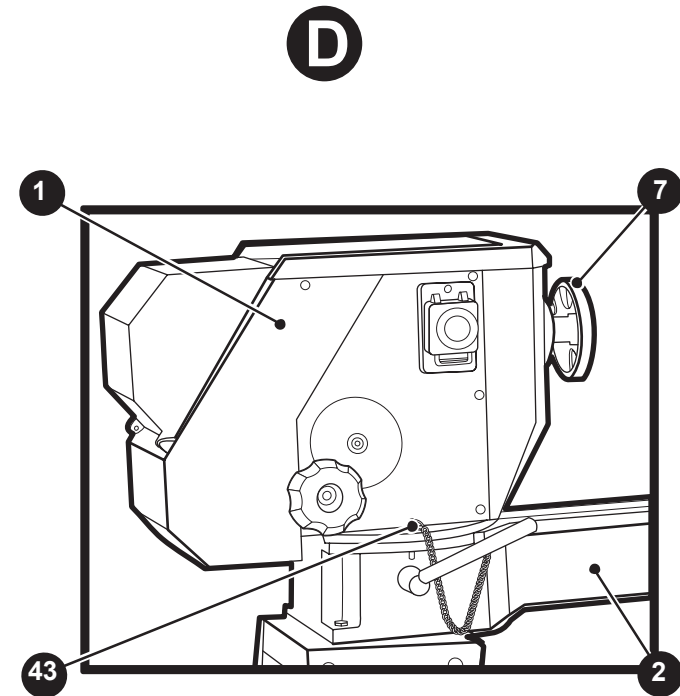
Рисунок D — общий вид станка с установленной на шпиндель планшайбой.
